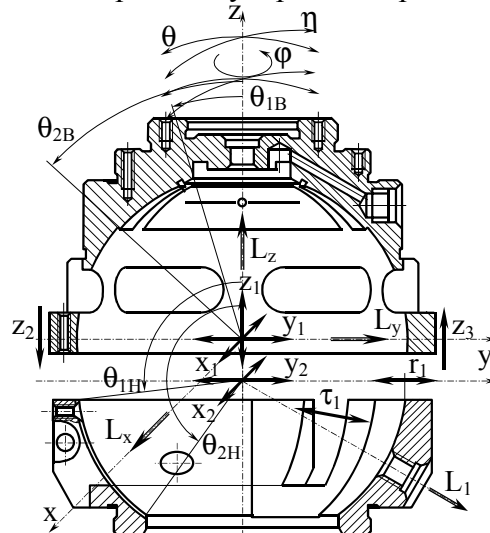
Схема відносних мікропереміщень корпусу і кришки опорного вузла при регулюванні зазору між сферичними поверхнями та зміні діаметрального зазору внутрішньої сферичної поверхні корпусу
